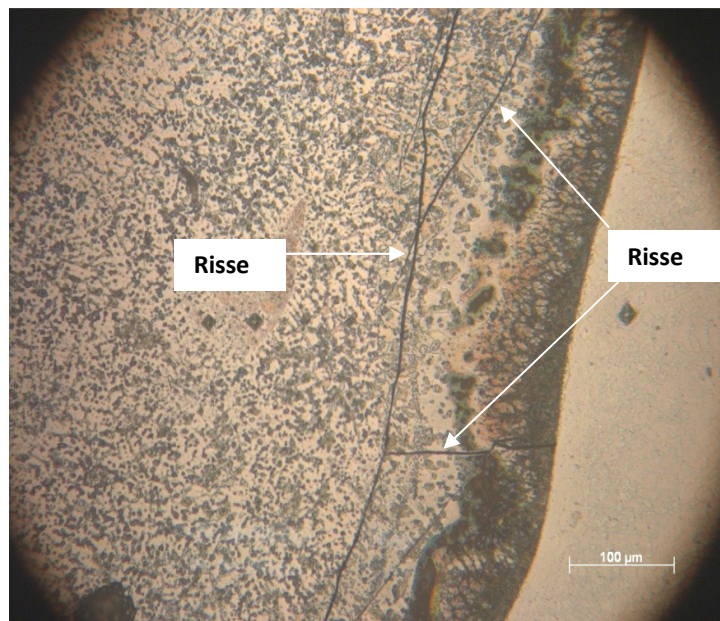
Al-Mg Schweißung - Querschliff 5-2
